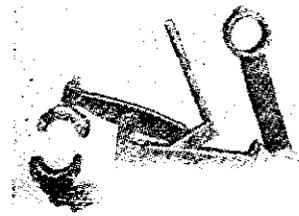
Шарнирный хомут станка фирмы Нортон для лепинга шеек коленчатого вала.
